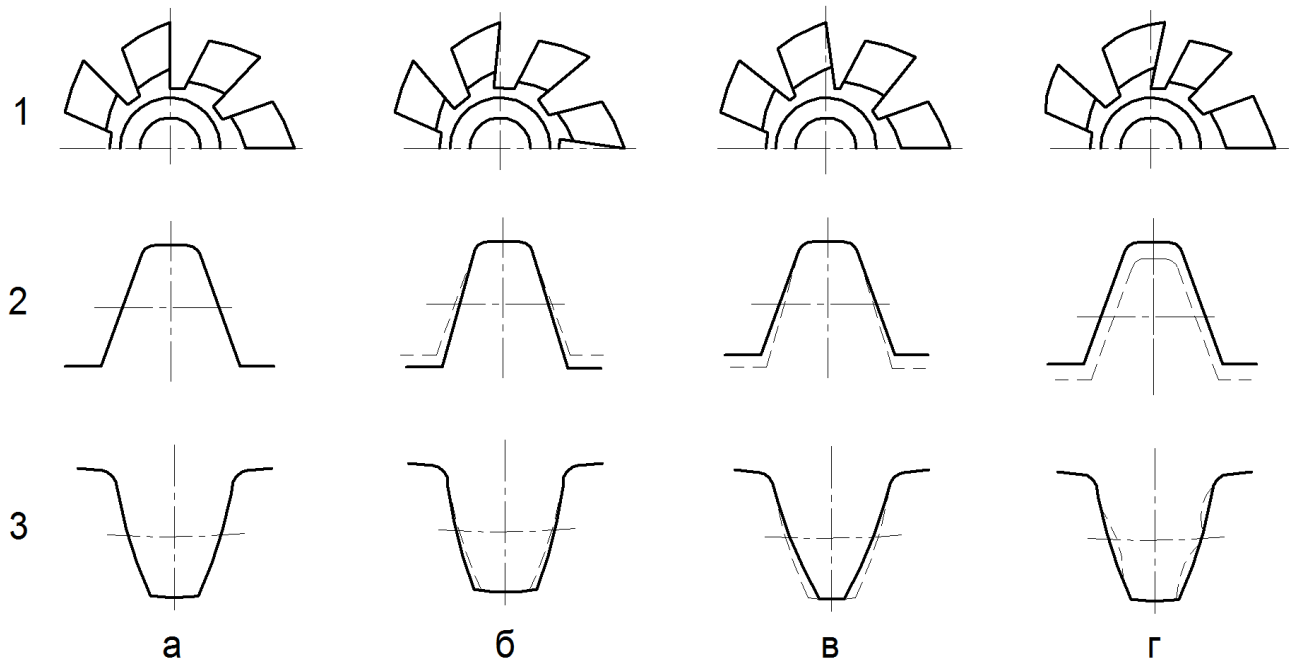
Схеми впливу розташування передньої поверхні зубців фрези на оброблюваний профіль
